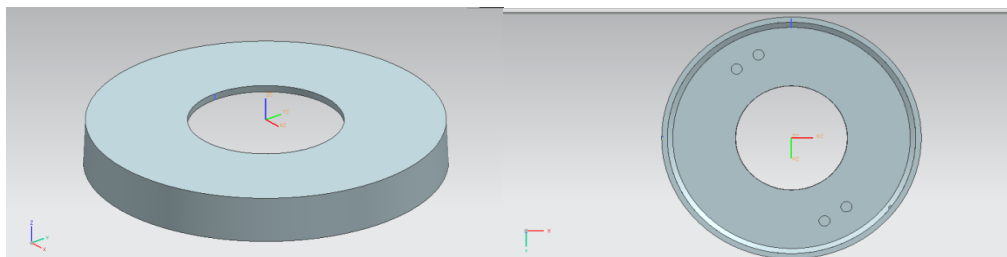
Anillo actuador superior, vista trimétrica (izquierda), vista inferior (derecha)
